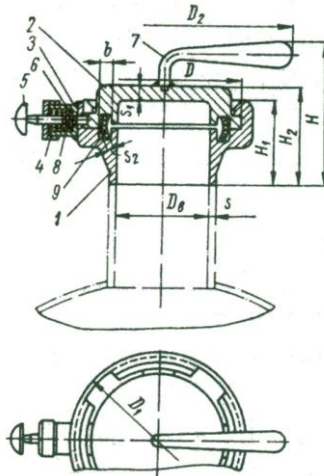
Конструкция круглых люков с байонетным затвором для стальных аппаратов на  $p_y = 1,6$  МПа, ОН 26-01-35-67: 1 – корпус; 2 – крышка; 3 – стакан; 4 – крышка стакана; 5 – фиксатор; 6 – штифт; 7 – рукоятка; 8 – пружина; 9 – прокладка
